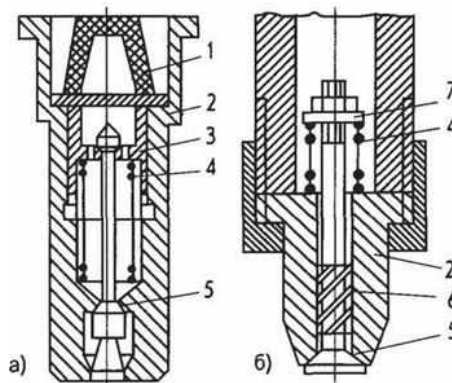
Розпилювачі клапанних форсунок:
